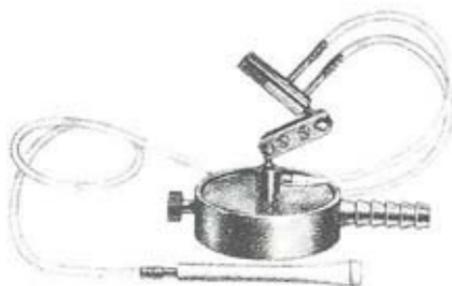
Mechero usado para el soldado.
